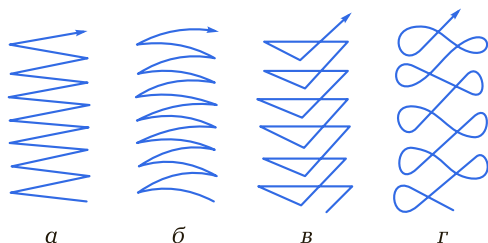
Направление колебательных движений электрода перпендикулярно оси шва при ручной дуговой сварке: а, б — обычный режим сварки; в, г — сварка с усиленным прогревом кромок
